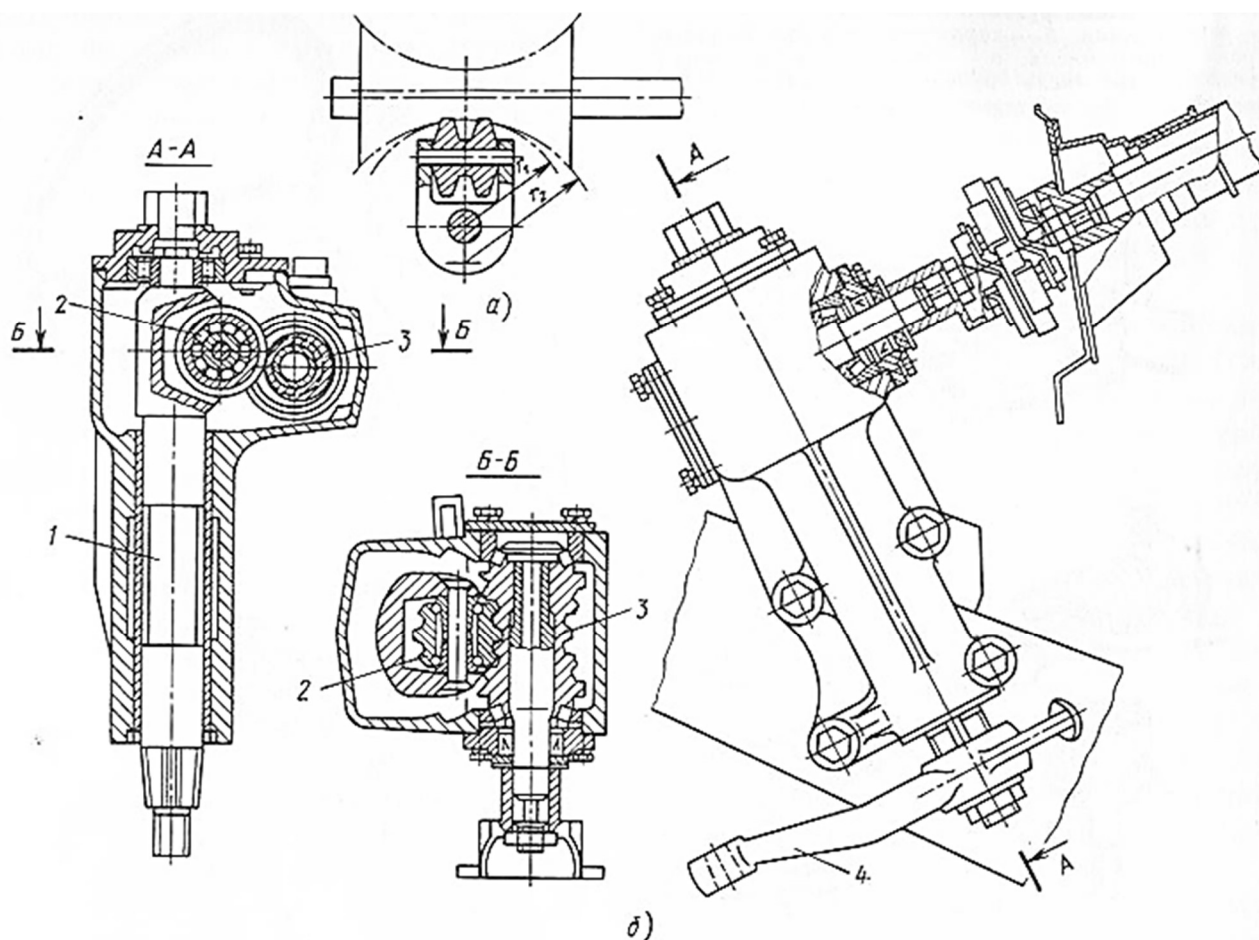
Червячно-роликовый рулевой механизм: *а* – схема; *б* – конструкция; *1* – вал сошки; *2* – трехгребневый ролик; *3* – глобоидный червяк; *4* – сошка.
